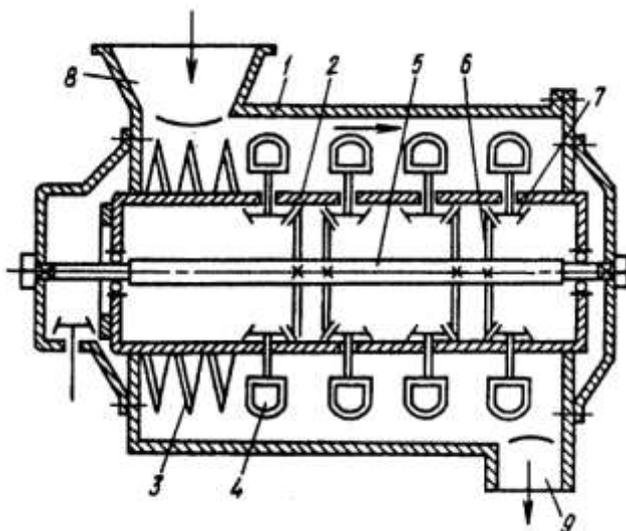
Тестомесильная машина: 1- корпус; 2 - вал; 3 - шнек; 4 - лопатки; 5 - ось; 6 - коническое колесо; 7 - коническая шестерня; 8 - загрузочное отверстие; 9 - разгрузочное отверстие
